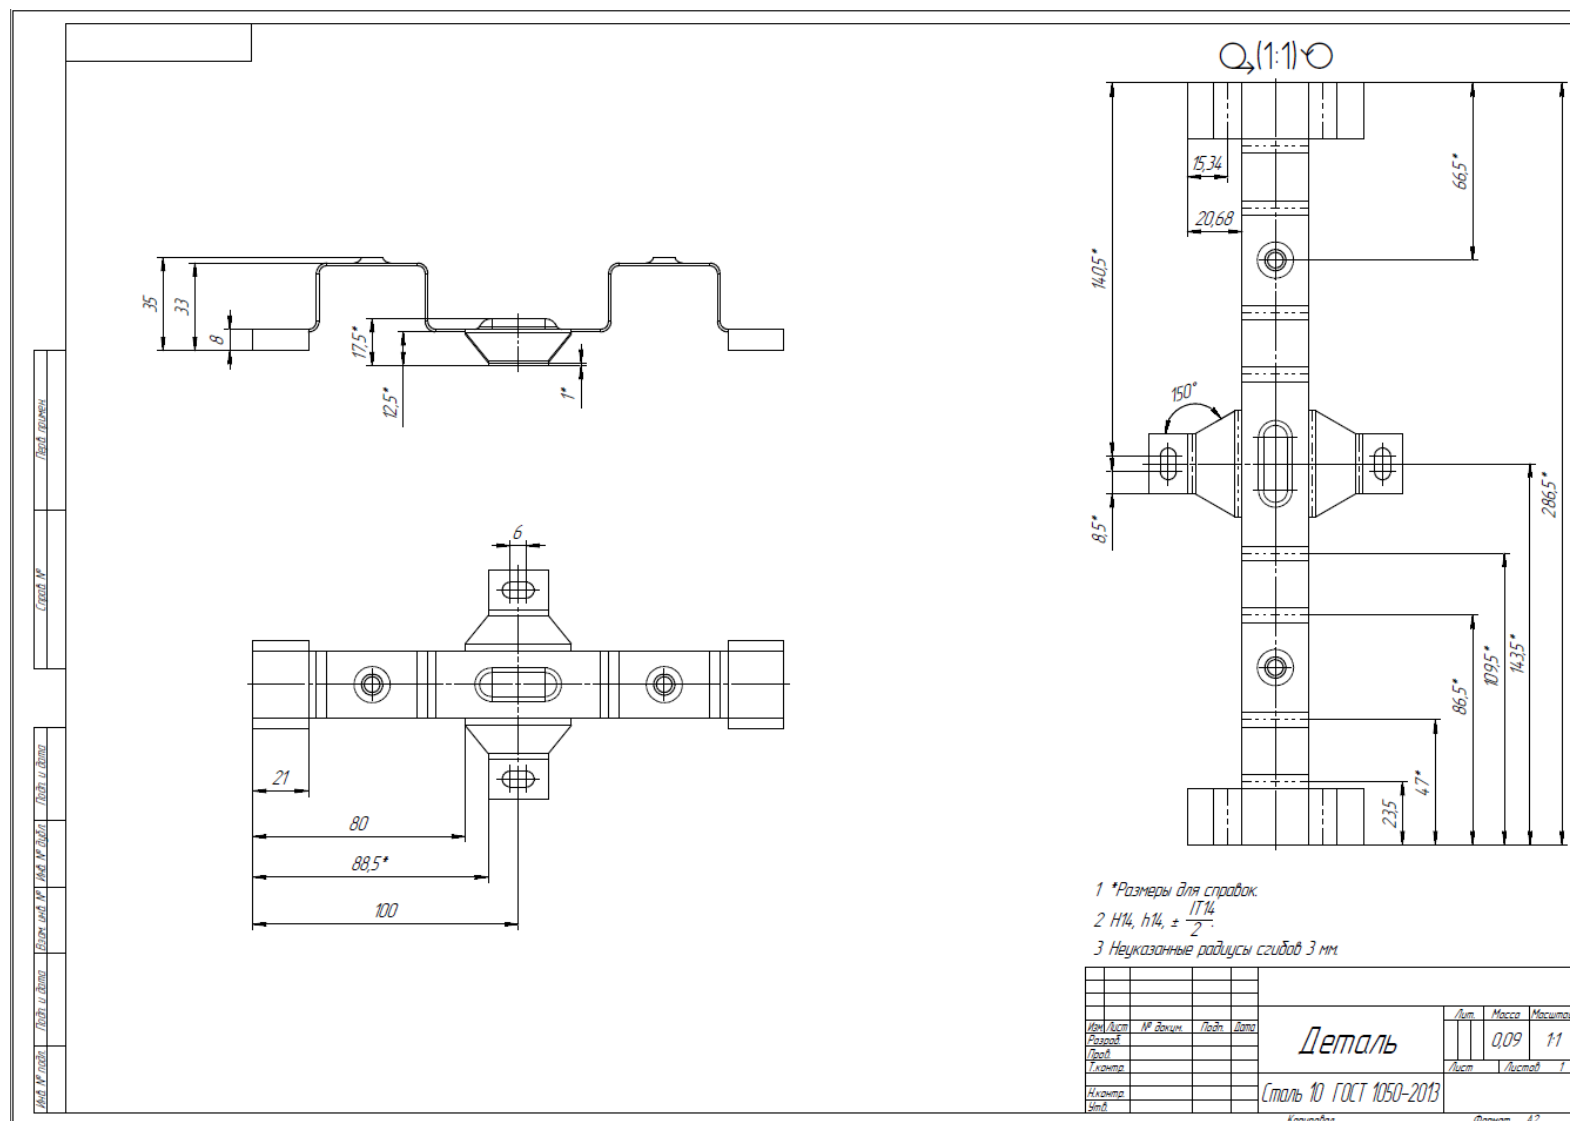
Чертеж детали «Кронштейн» (вариант 4)
